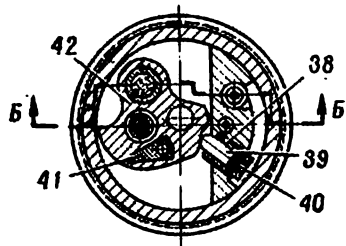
Устройство взрывателя (положение деталей взрывателя в служебном обращении):
